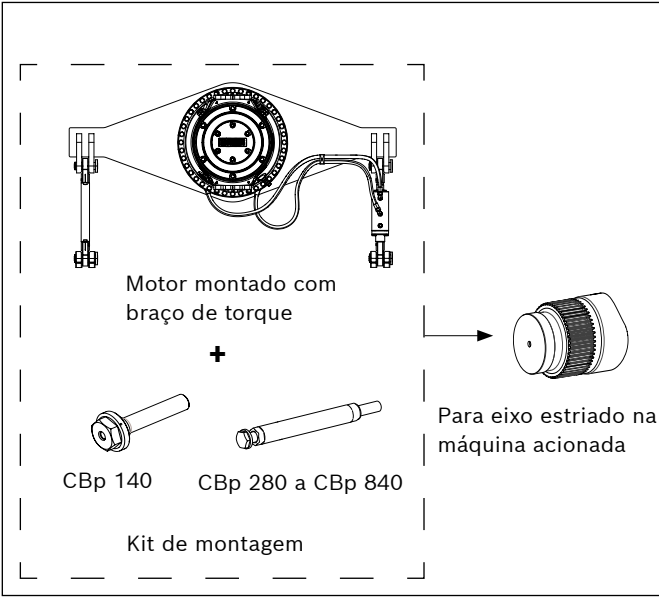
Montagem do braço de torque de duas terminações para eixo estriado
